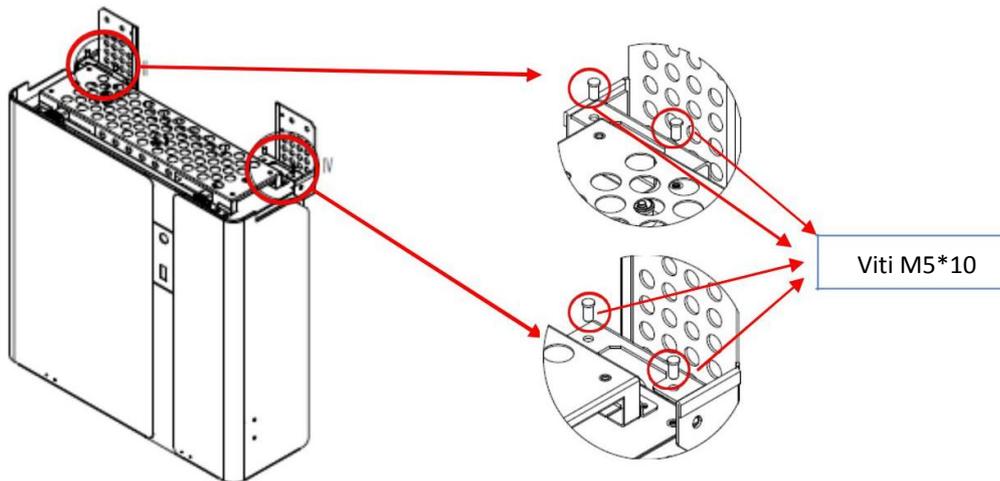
Assemblaggio delle staffe di fissaggio modulo batteria
